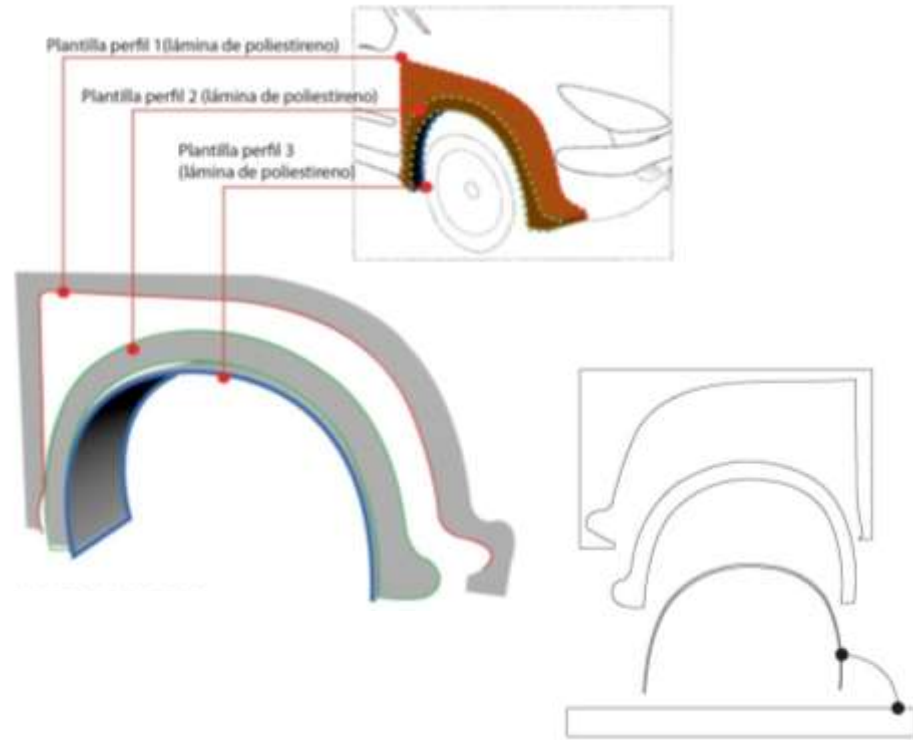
Fase 2 – Dibujo de plantillas delanteras
